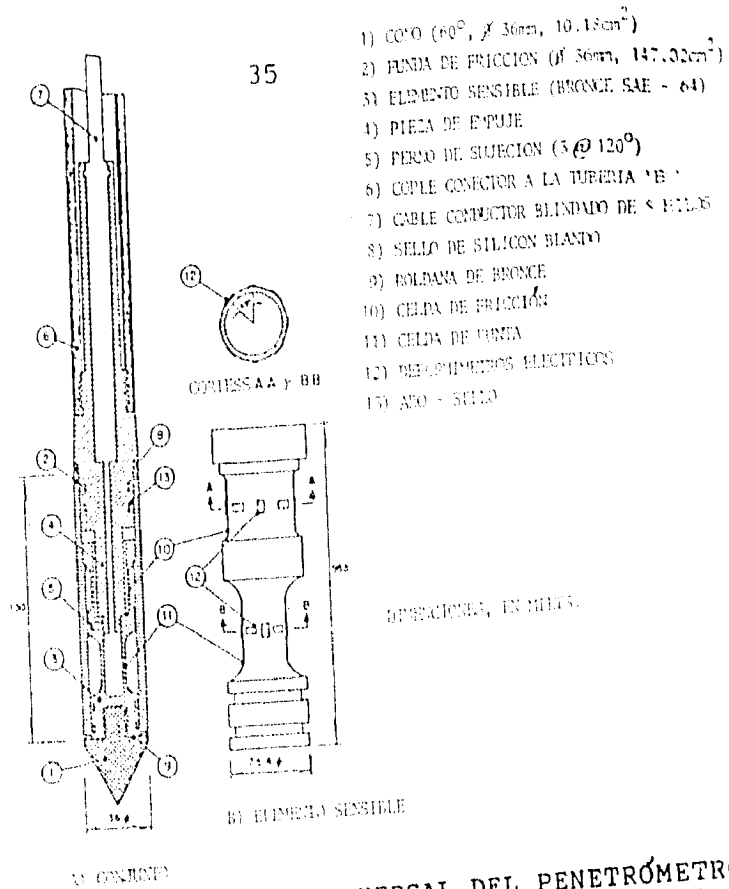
CORTE TRANSVERSAL DEL PENETRÓMETRO ESTÁTICO TIPO ELÉCTRICO (REF. 7).
